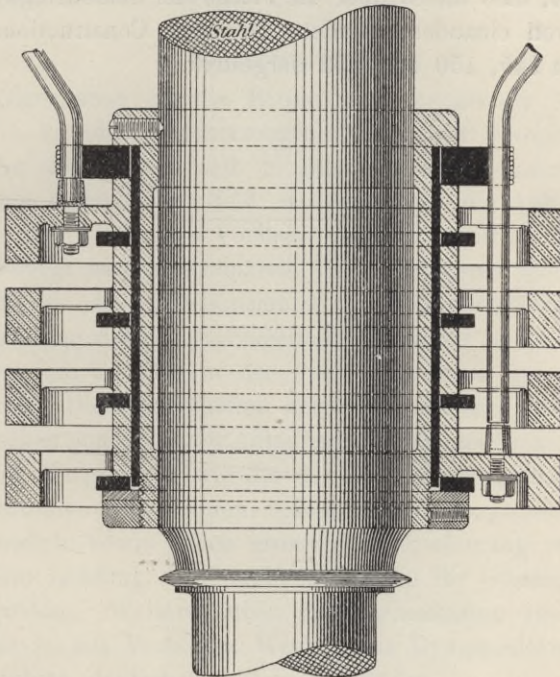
Bauart der Schleifringe einer zweiphasigen Wechselstrommaschine.
